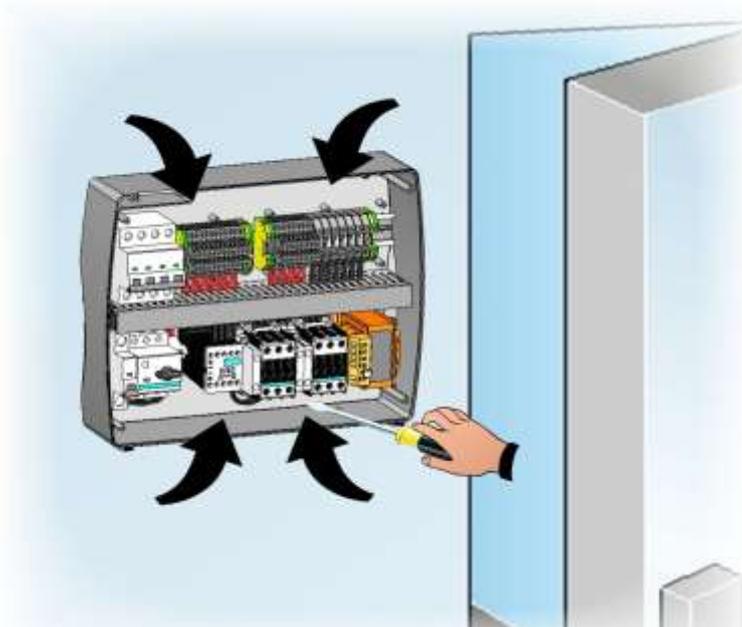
Bohrungen des Bodens drücken, um die Öffnungen für die Befestigung des Schaltkastens zu erstellen.
